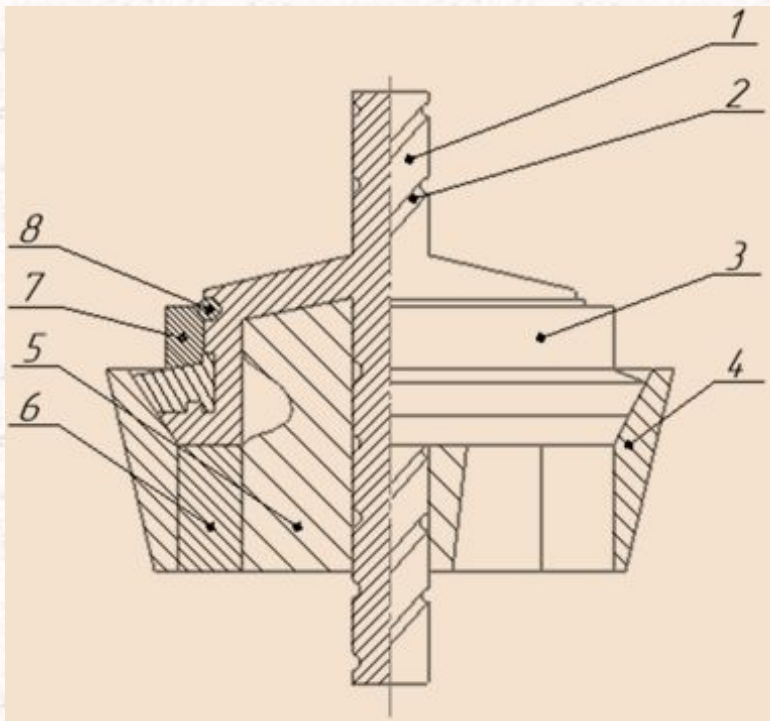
Насосный клапан (1 – шток; 2 – канавка; 3 – корпус; 4 – седло; 5 – стол; 6 – диск; 7 – кольцо; 8 – стопорное кольцо)
